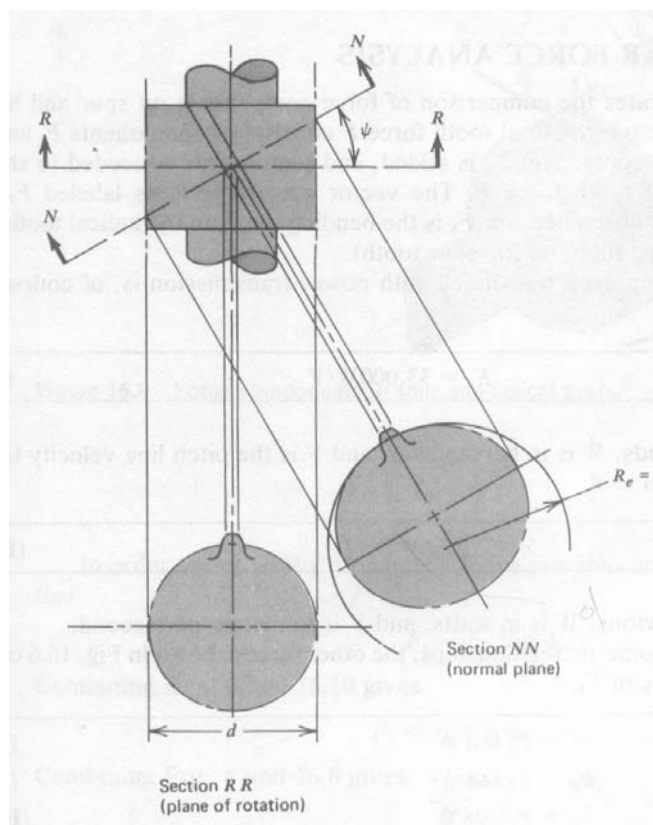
corte em engrenagens cilíndricas helicoidais
